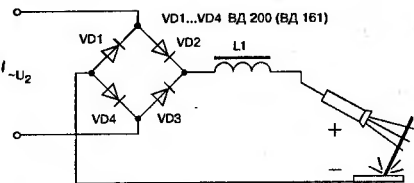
Принципиальная электрическая схема мостового выпрямителя сварочного аппарата, с указанием полярности при сварке тонколистового металла
